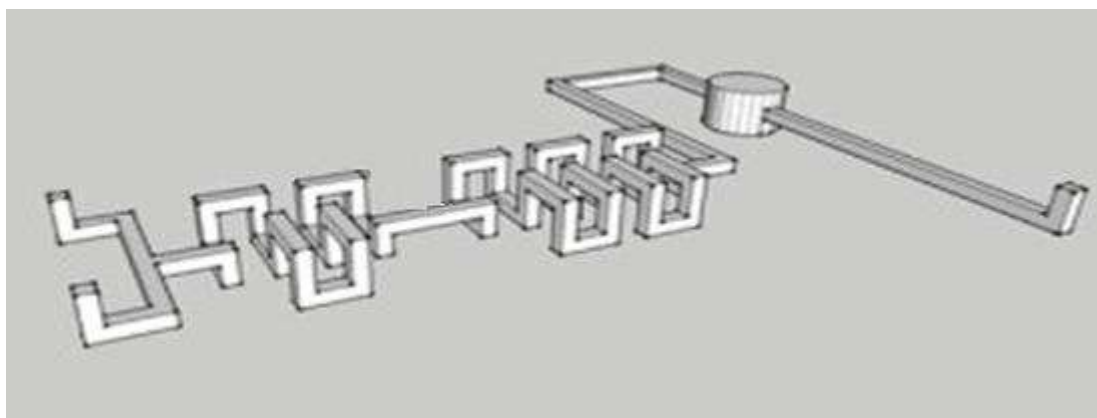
Estrutura interna do dispositivo construído com LTCC.
